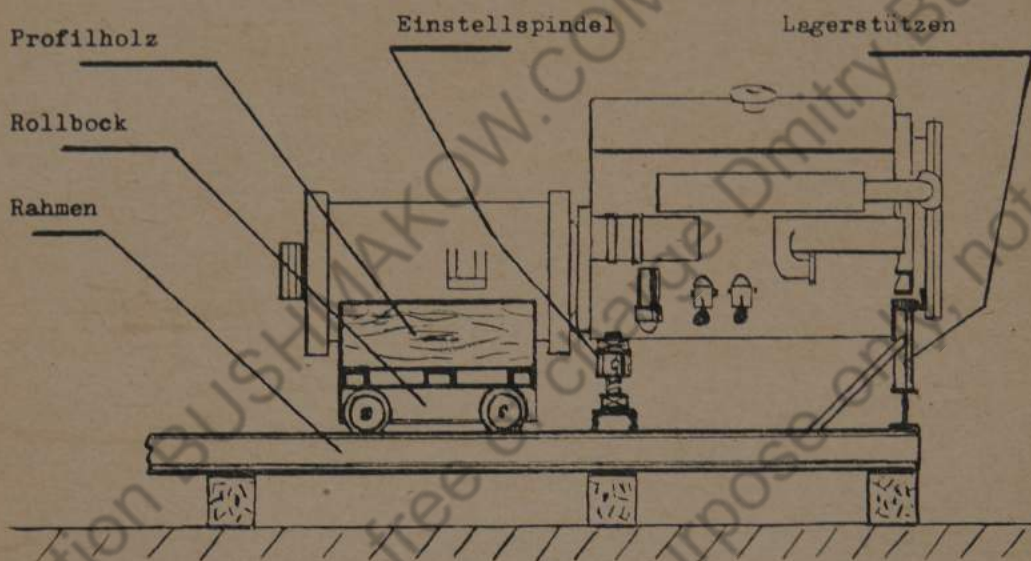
Otto-Motor und Stromerzeuger auf Montagebock
